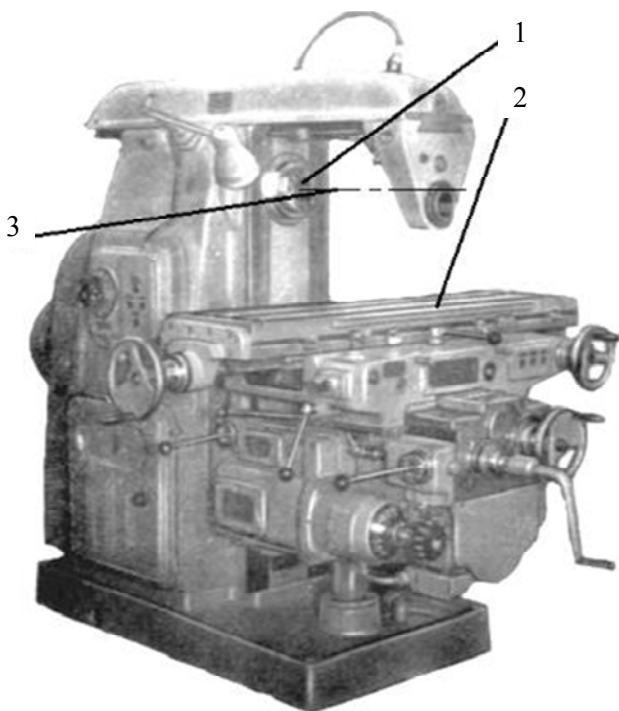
Общий вид горизонтально-фрезерного станка модели 6M82Г
